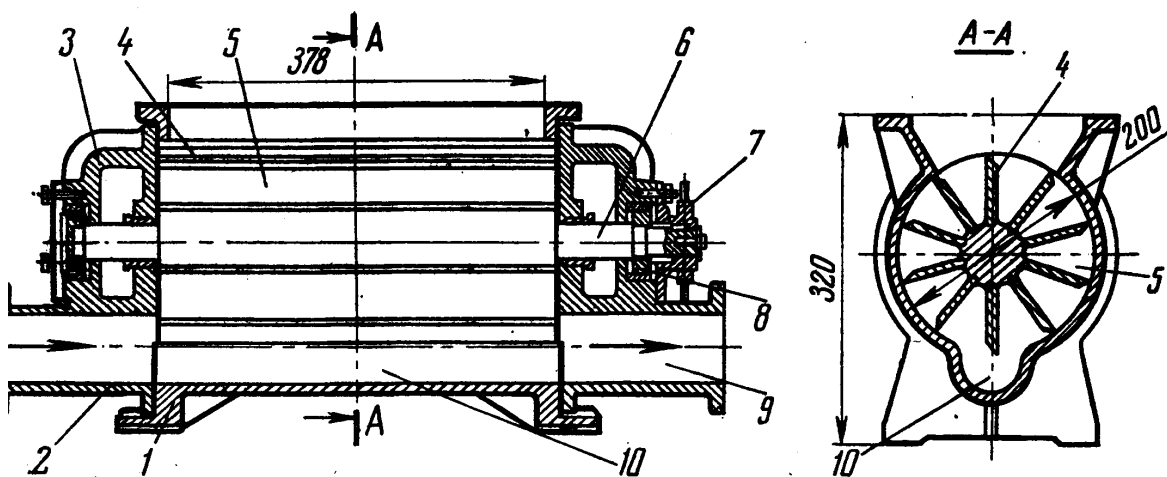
Роторний живильник: 1 – чавунний корпус; 2 – патрубок для стисненого повітря; 3 – бокова кришка; 4 – поздовжні перегородки, 5 – ротор, 6 – вал ротора; 7 – привідна зірочка; 8 – опорні шарикопідшипники; 9 – патрубок борошняно-повітряної суміші. 10 – пневмоканал.
